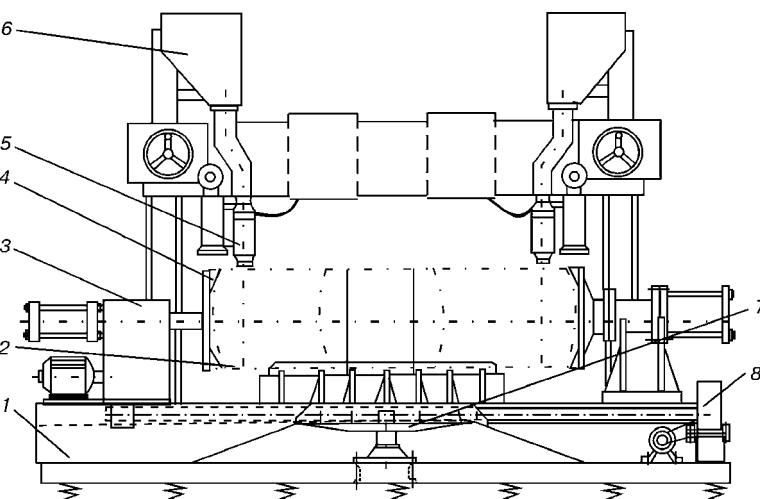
Схема специализированной установки для сварки под слоем флюса одновременно двух кольцевых швов: 1 — станина; 2 — резервуар; 3 — привод вращения резервуара; 4 — захват; 5 — сварочная головка; 6 — бункер для флюса; 7 — стол подъемный; 8 — привод поднятия резервуара
